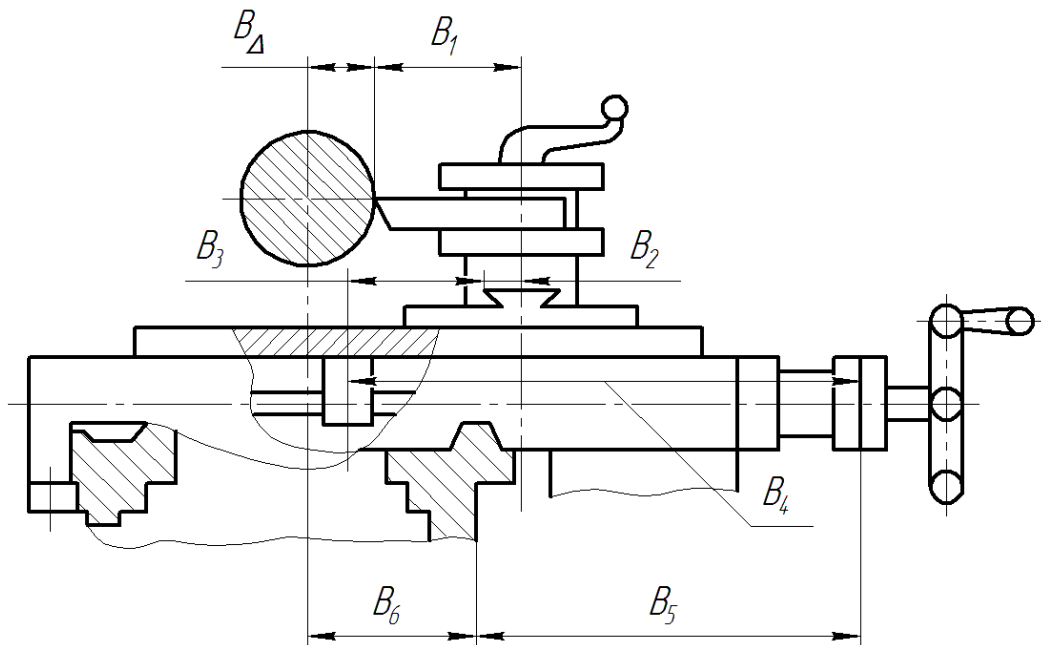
Розмірний ланцюг B , що визначає розмір B_{Δ} радіуса валика, який виготовлений на токарному верстаті
